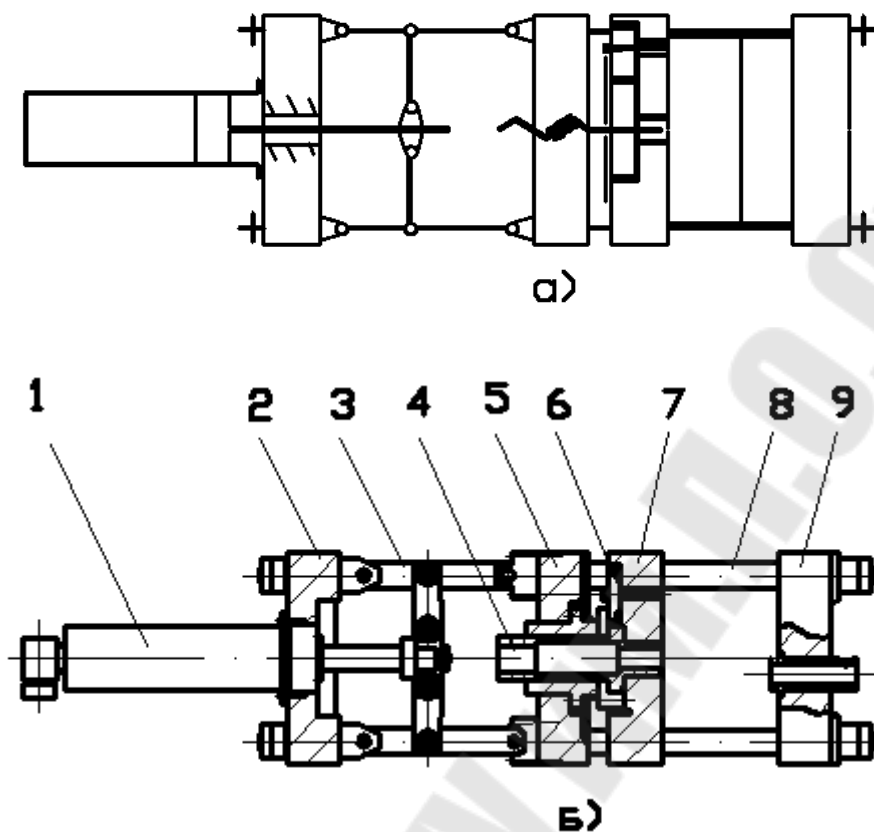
Кинематическая (а) и конструктивная (б) схемы рычажного запирающего механизма с центральным винтовым механизмом настройки машины мод. 5А12: 1 - гидроцилиндр; 2 - задняя плита; 3 - рычажный механизм; 4 - силовой винт; 5 - подвижная плита; 6 - шестерня; 7 - дополнительная подвижная плита; 8 - направляющие (колонны) машины; 9 - передняя плита
